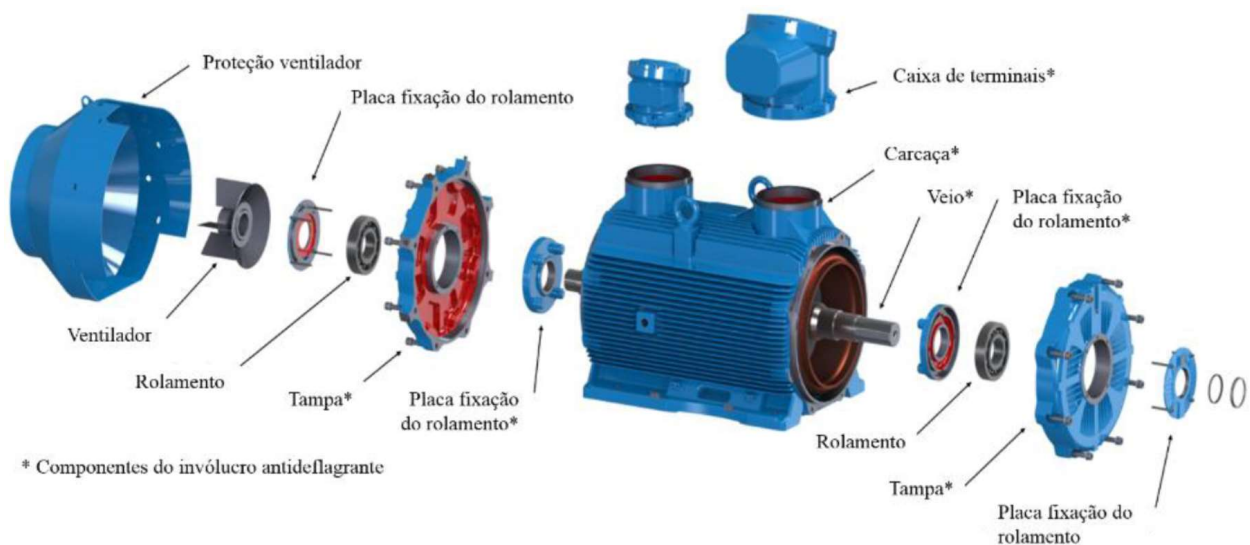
Vista explodida de um motor de indução trifásico antideflagrante
